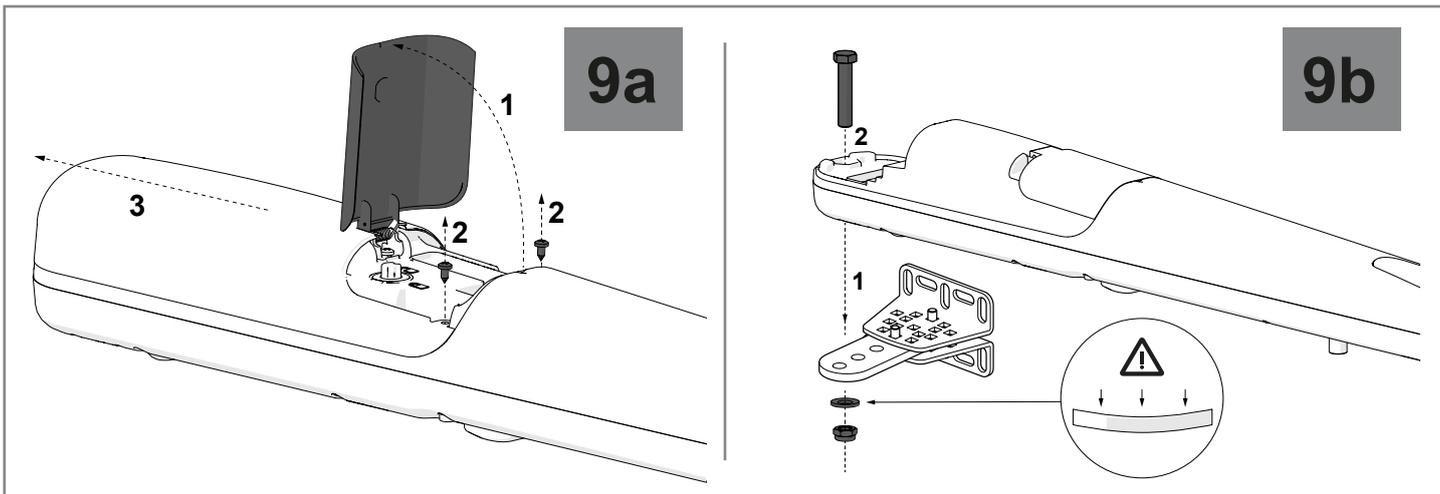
IT - Fissaggio motoriduttore e staffa anteriore
